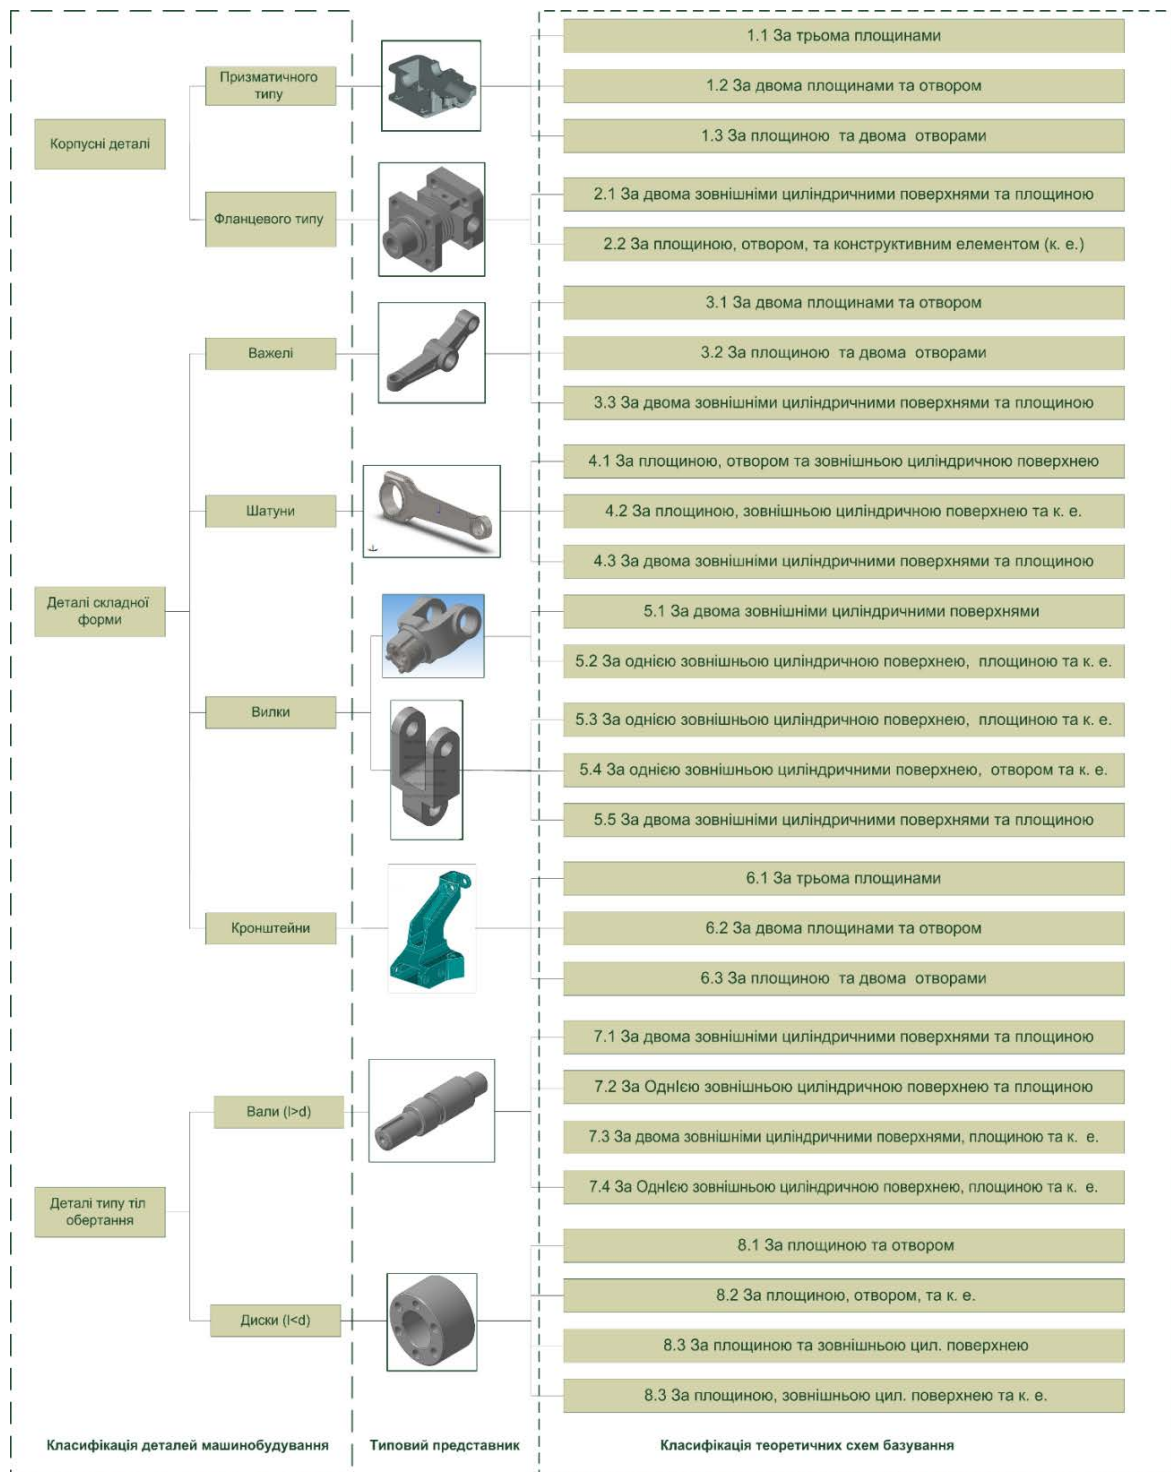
Взаємозв'язок геометричної форми обробленої деталі та схеми базування
